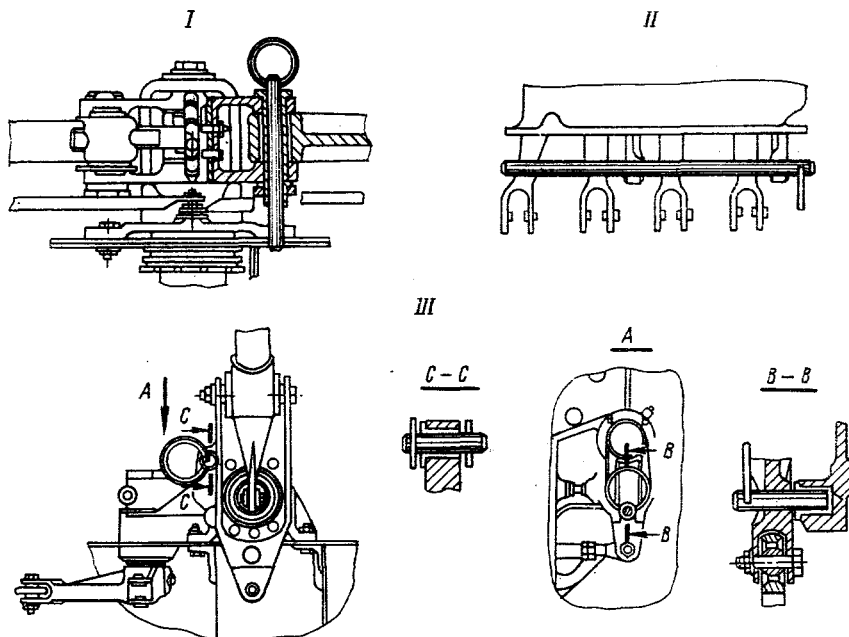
Установка штырей для крепления педалей и рычагов управления вертолетом в нейтральном положении:
